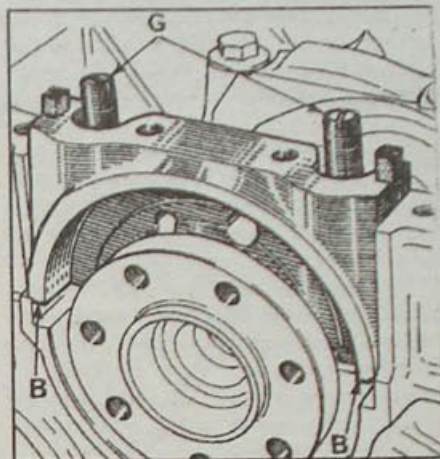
Центрирование крышки коренного подшипника №1 с помощью двух шпилек (G) и место (B) нанесения герметика CAF 4/60 Thixo
